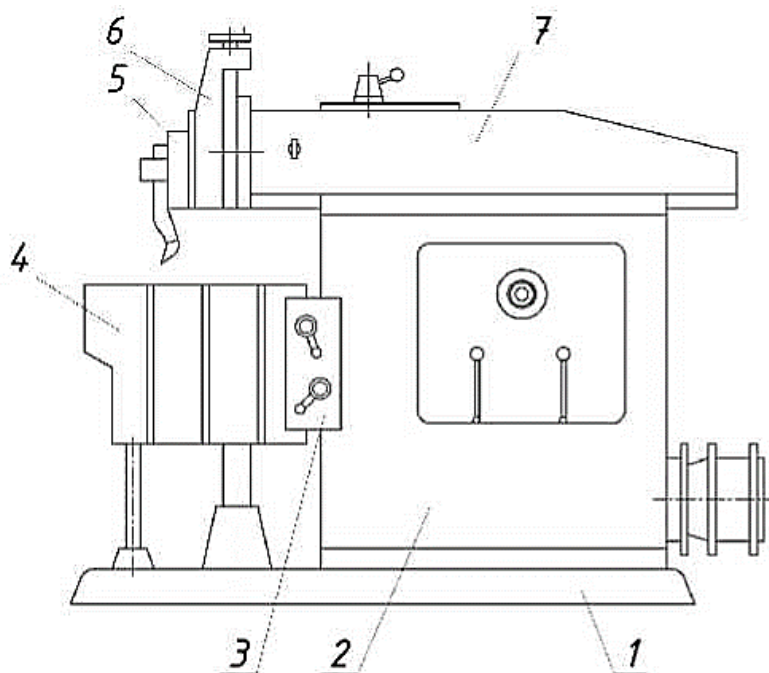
Загальний вигляд поперечно-стругального верстата
